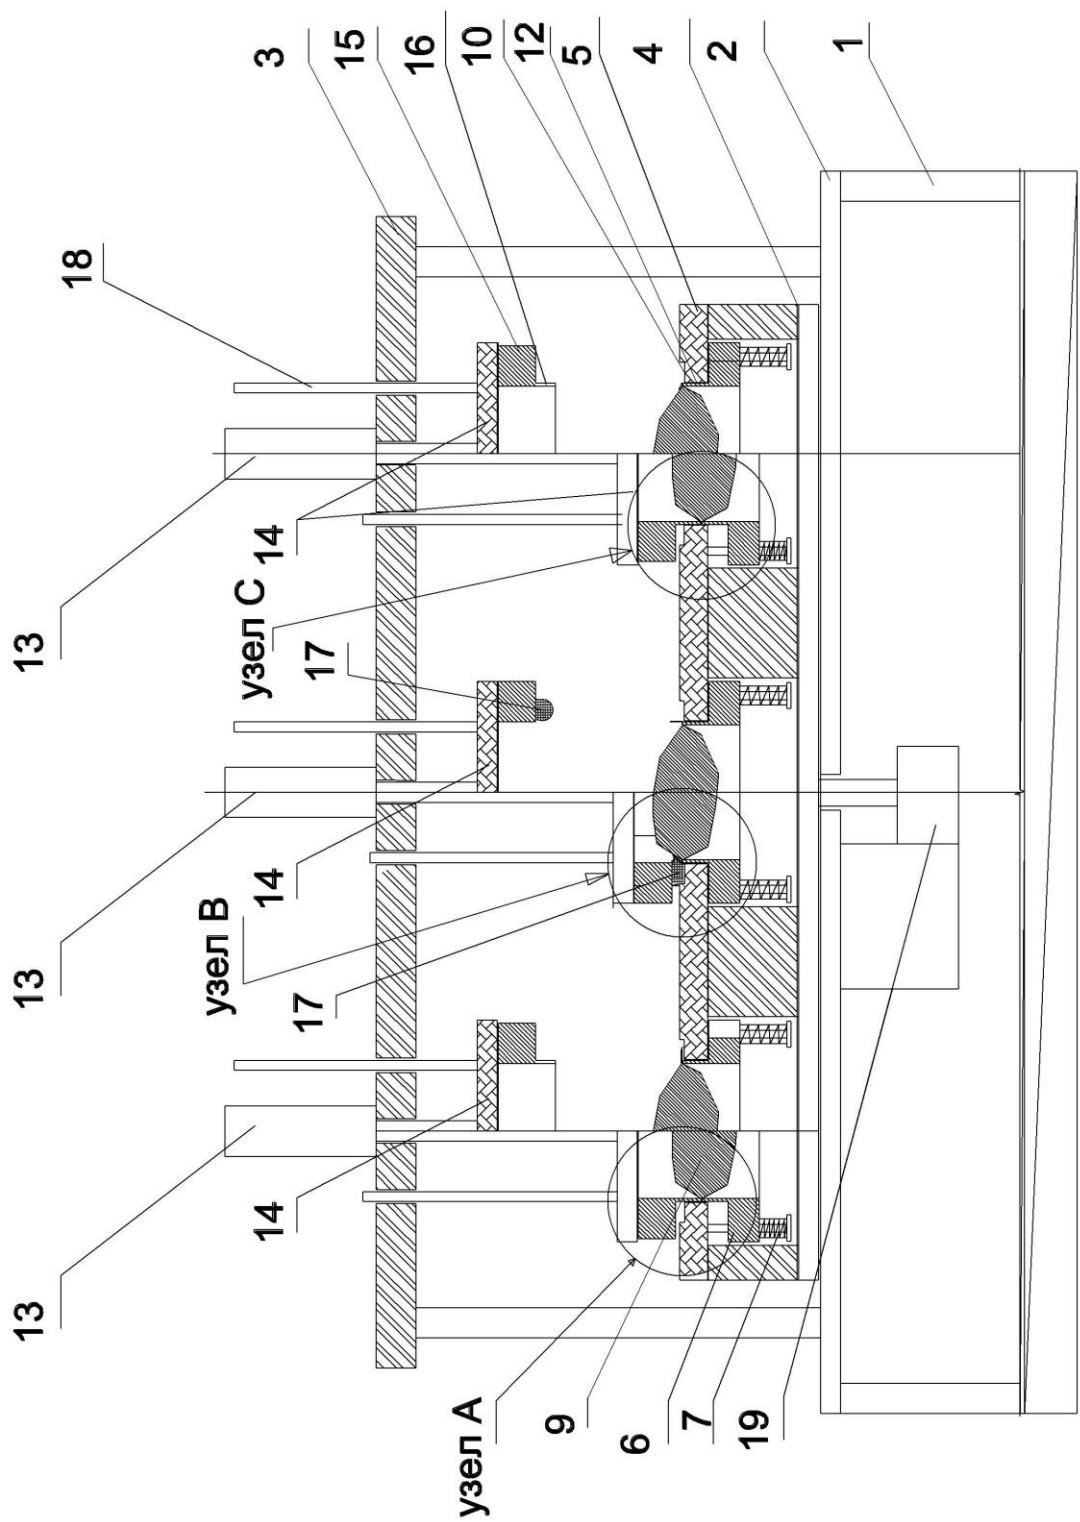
Общий вид станка для упаковки изделий в отформованной фольге во время и после осуществления формовки на каждой стадии
